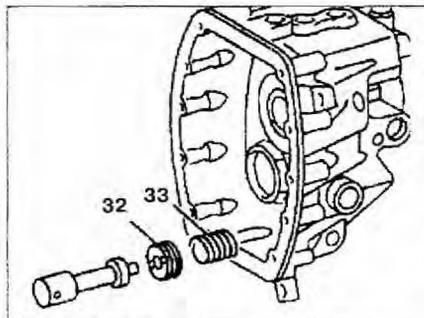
Выкрутите резьбовую втулку 32 из корпуса коробки передач и снимите пружину 33.
